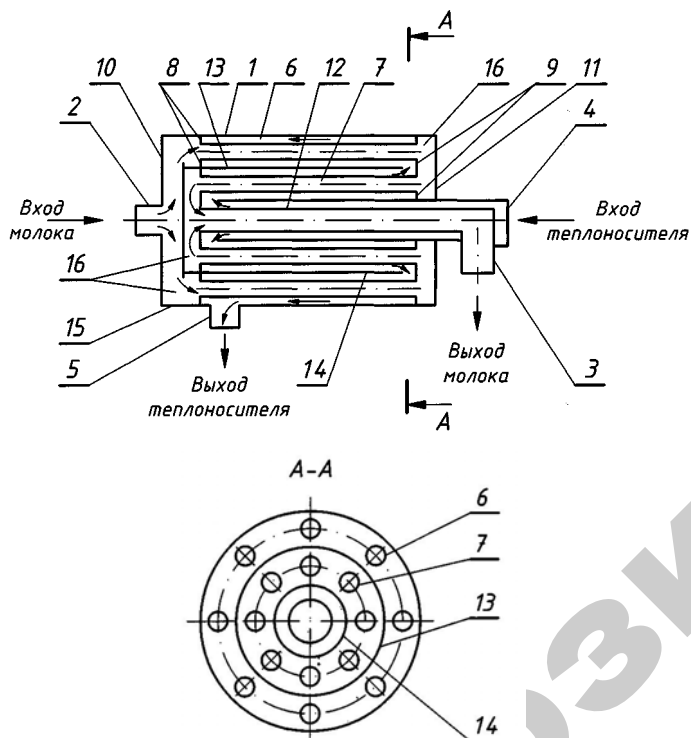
Принципиально-конструктивная схема теплообменника: 1 – корпус; 2 – патрубок входной; 3 – патрубок выходной; 4 – патрубок впускной; 5 – патрубок выпускной; 6 – трубы наружные; 7 – трубы внутренние; 8, 9 – решетки трубные; 10, 11 – крышки; 12 – труба центральная; 13, 14 – перегородки цилиндрические; 15 – коллектор входной; 16 – полость кольцевая
